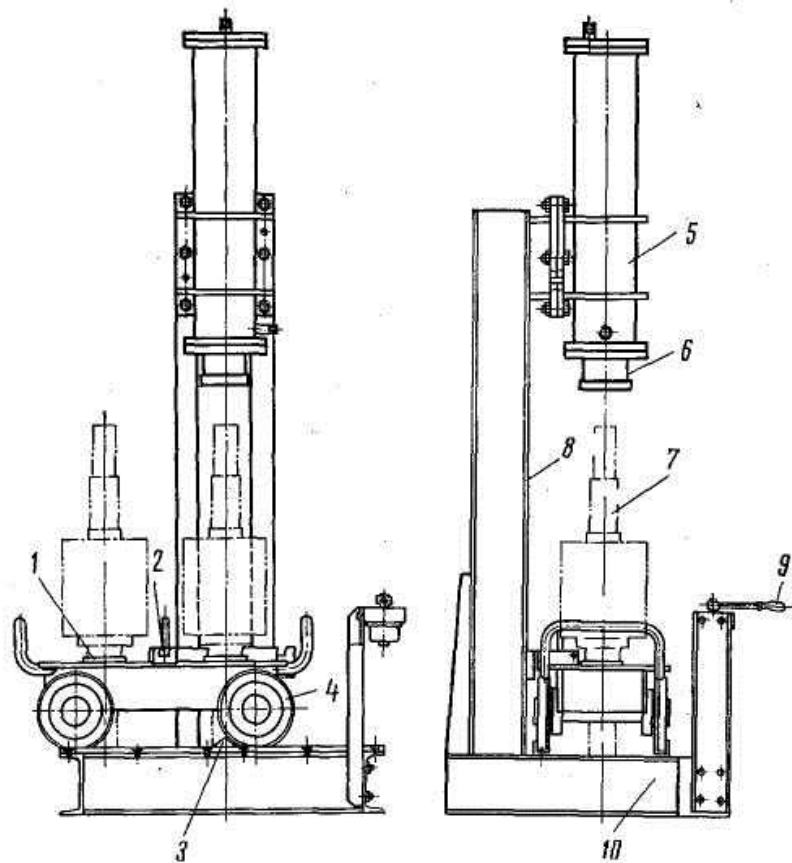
Пневматичний прес для шихтування пакетів сердечників на вал якоря
